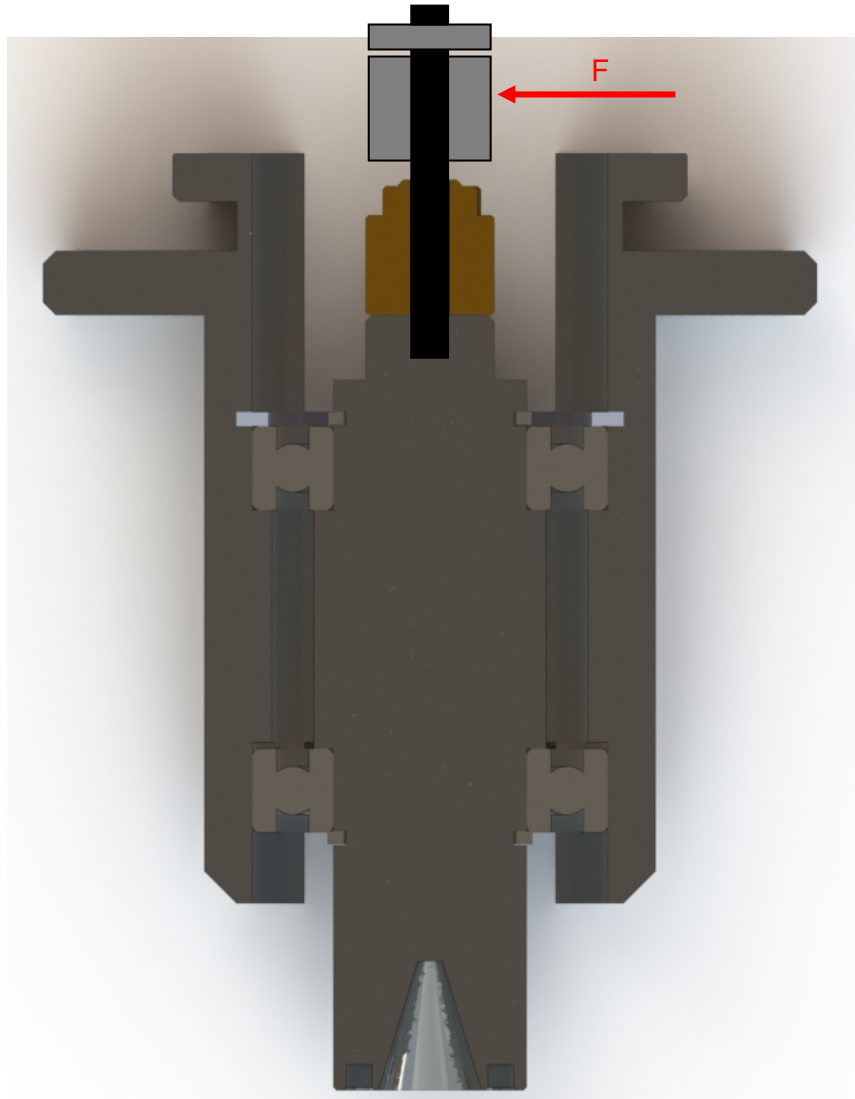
Werkzeughalter 1 Schnittansicht 3
